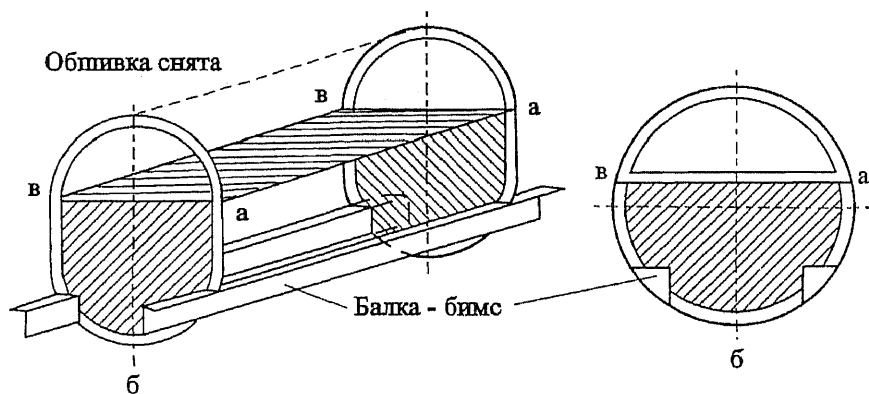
Силовая схема усиления фюзеляжа в зоне больших вырезов; ава, авб — горизонтальная и вертикальная силовые пояса каркаса
